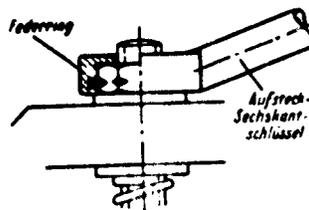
Aufsteck-Sechskantschlüssel mit Federring für Vorrichtungen
